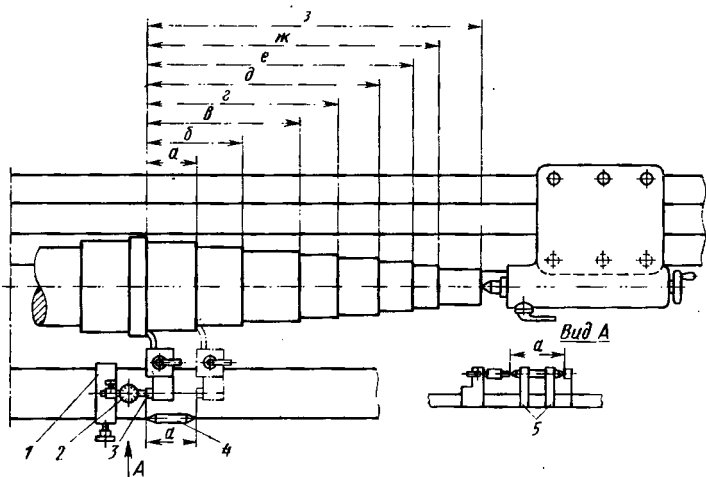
Приспособление с индикатором для обработки и измерения длин ступеней вала
